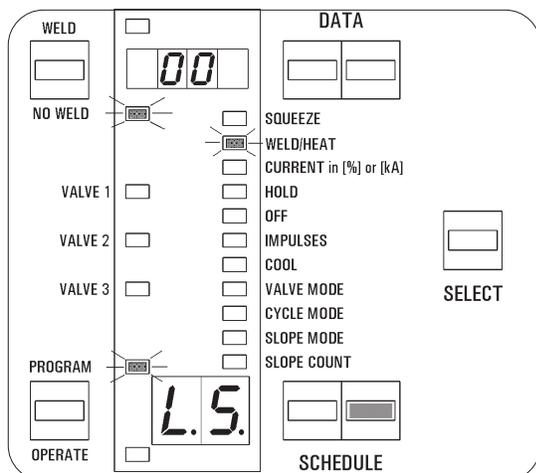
Programe CONTEO DE SOLDAR DE SOLDAR
